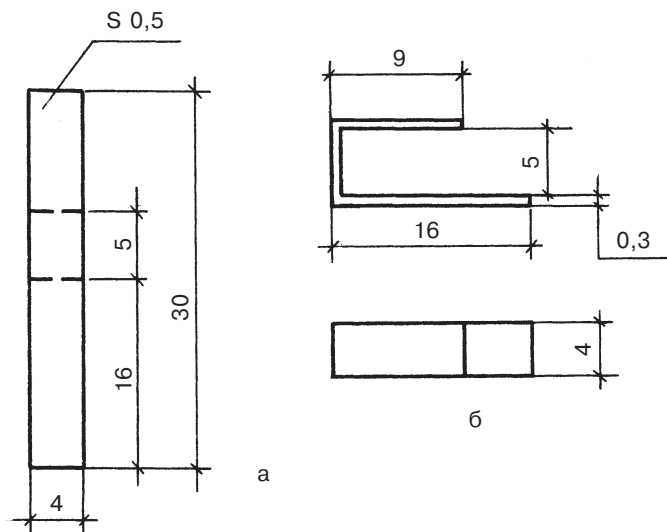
Лепесток: а — заготовка; б — готовое изделие
